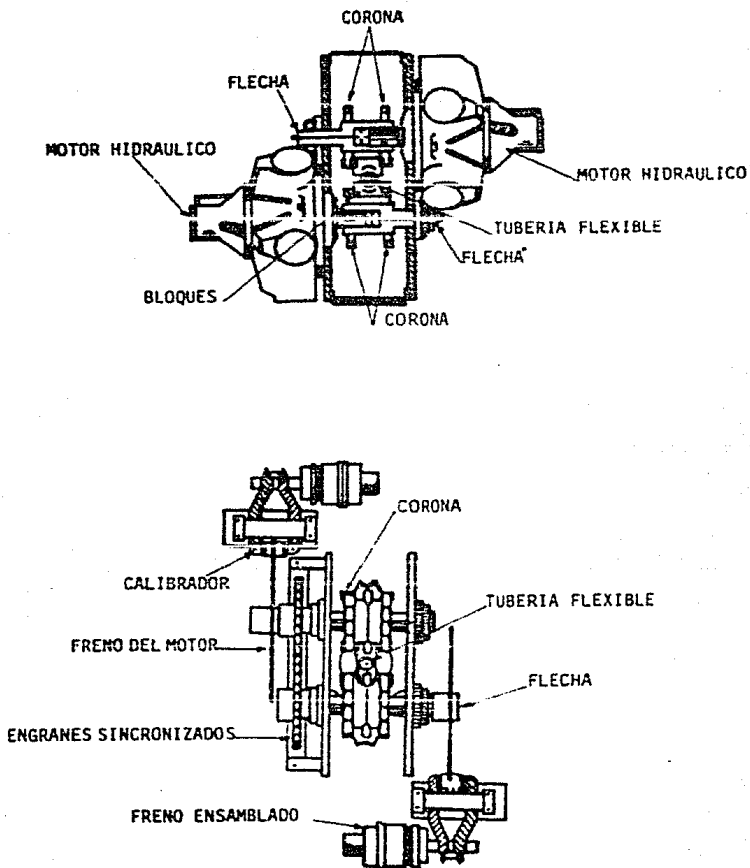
PRINCIPALES COMPONENTES DE LA CABEZA INYECTORA
